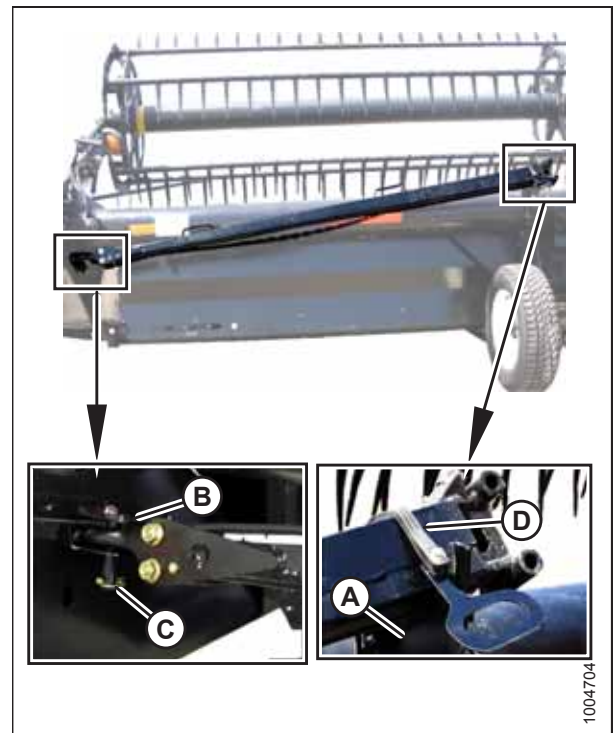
Remoción de la barra de remolque - Lado izquierdo
